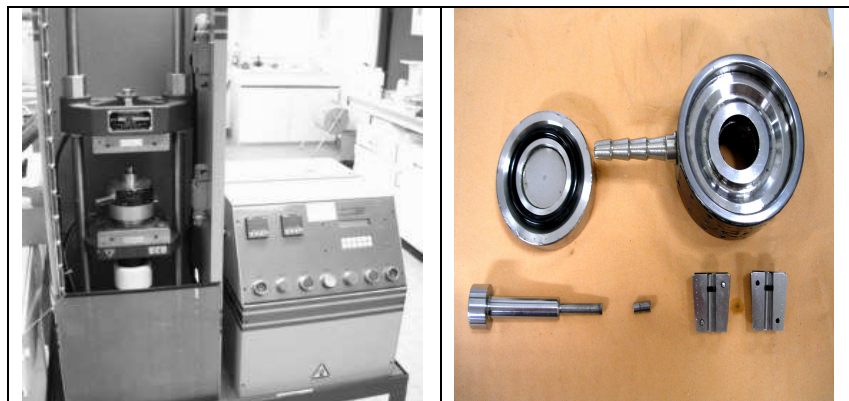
Presse uniaxiale Carver et le moule de pressage
